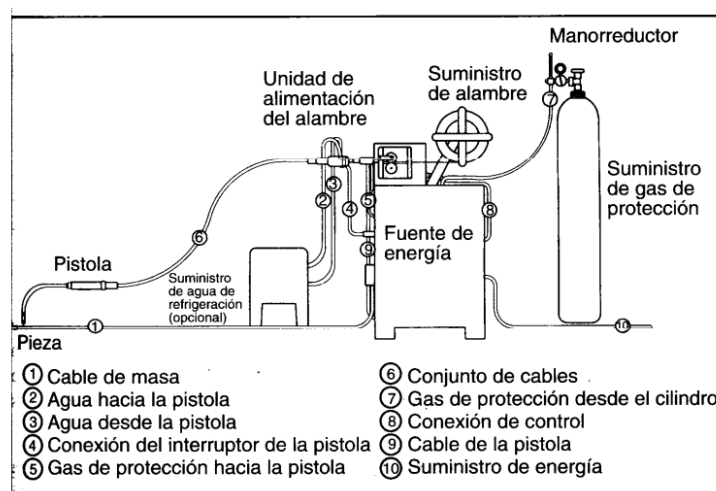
Equip de soldadura MIG/MAG. Apunts Tecnologia Mecànica.
